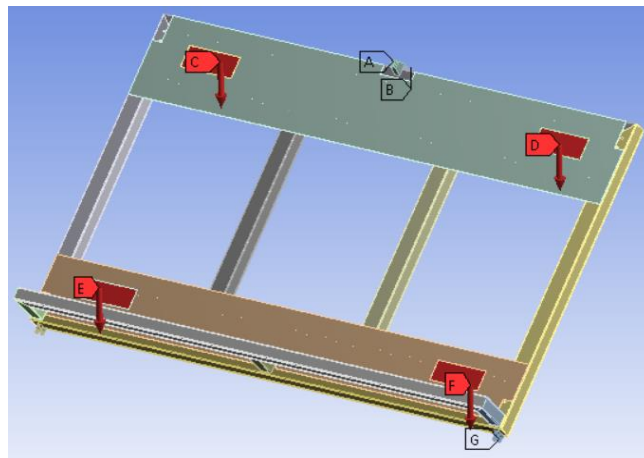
Ubicación de cargas y apoyos en la estructura del piso
